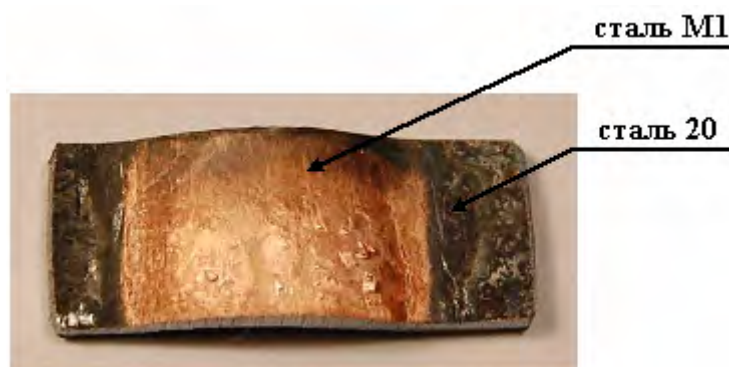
Излом сварного соединения «сталь 20 + медь М1»
